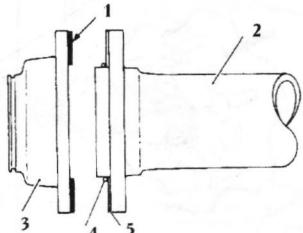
Нанесите тонкий ровный слой силиконового герметика на указанный участок корпуса подшипника
